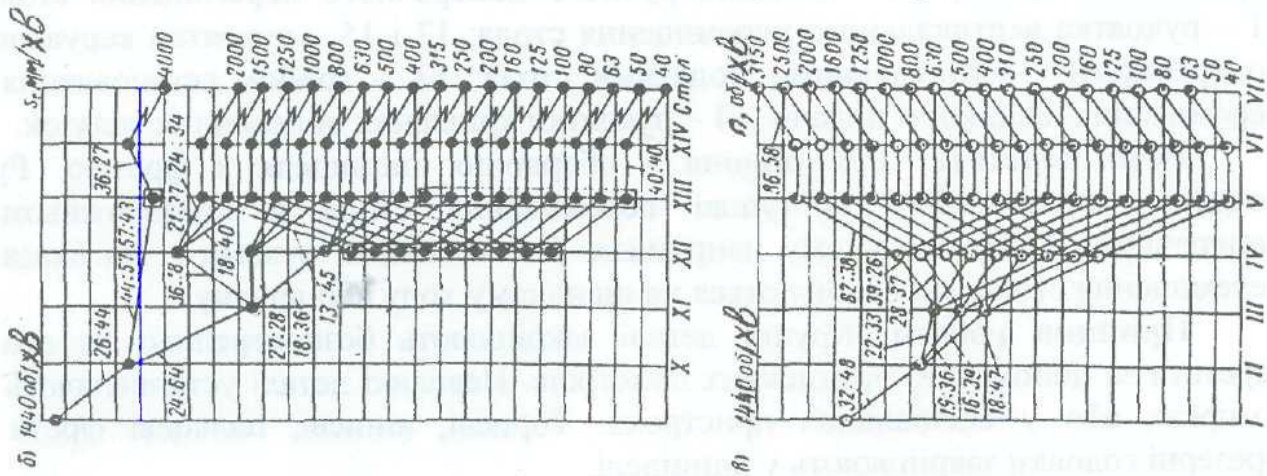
Кінематична схема вертикально-фрезерного верстака
